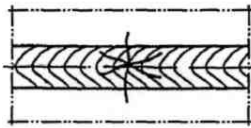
12. Радиальные трещины сварного соединения
